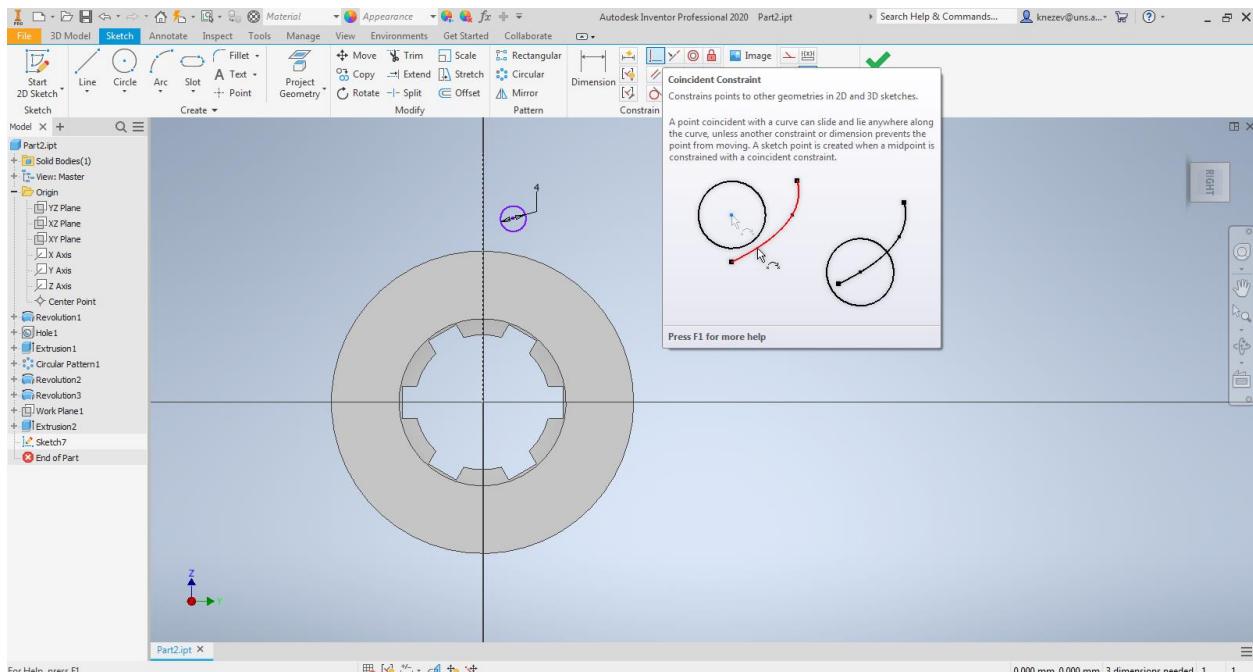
Izvlačenje (oduzimanje) profila za žleb za klin
